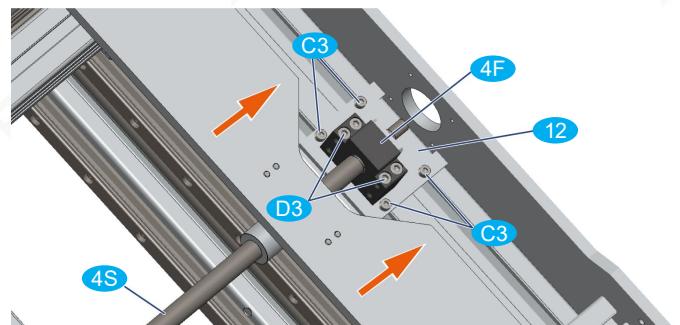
Festziehen Festlager und Flanschplatte X-Achse
